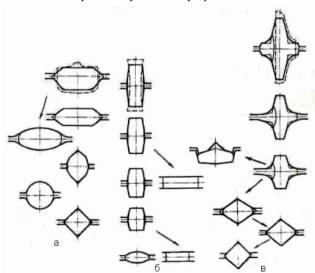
Схемы калибровок валков для прокатки головки (а), шейки (б) и подошвы (в) рельса
